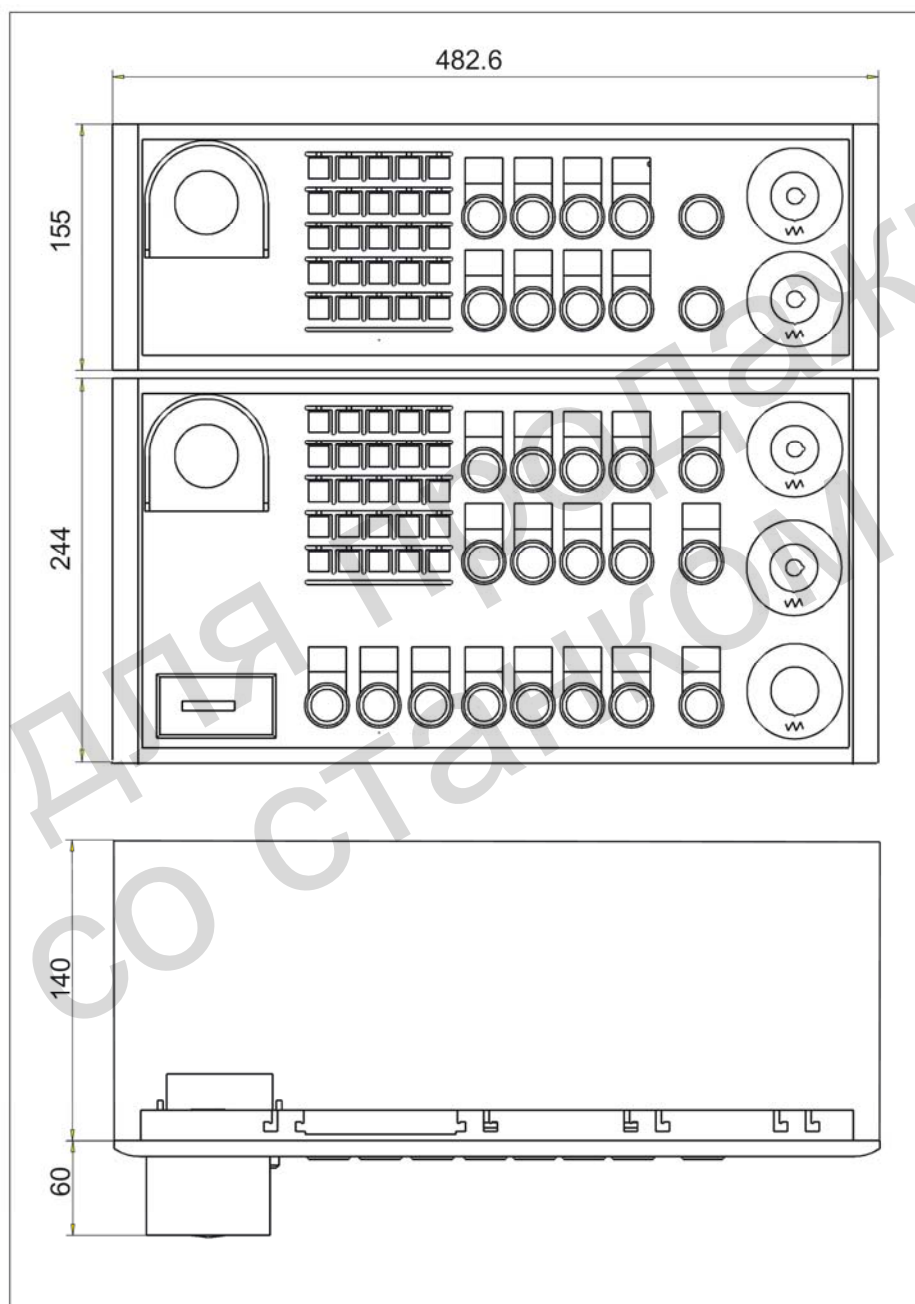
Габаритный чертеж MPP 483 и MPP 483L
